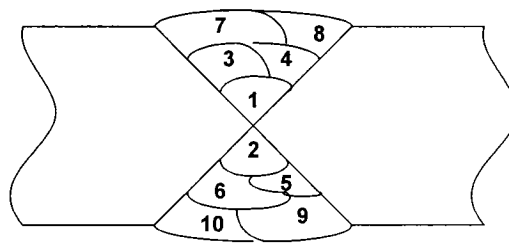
Soudage à passes multiples – Joint bout-à-bout
